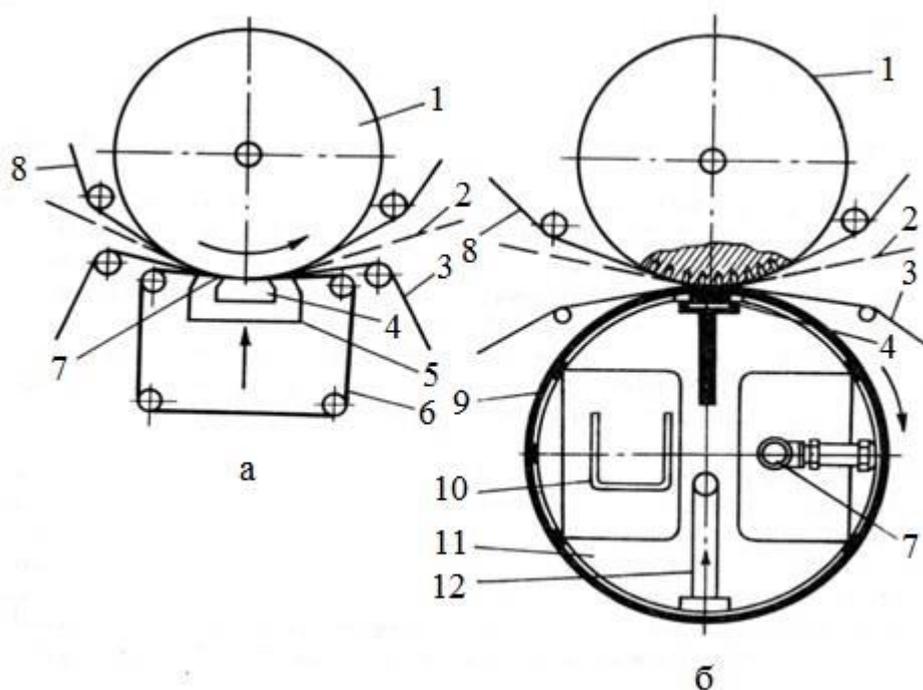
Схемы прессов с расширенной зоной прессования:
